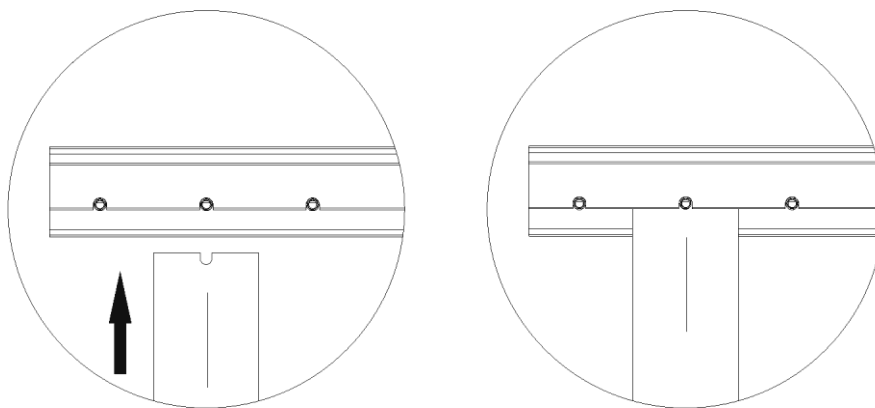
Einsetzen des Mono Connector Boards, exemplarisch
